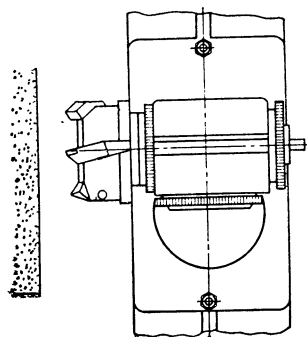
Схема начального положения торцевой фрезы и шлифовального круга при заточке задней поверхности зуба:
